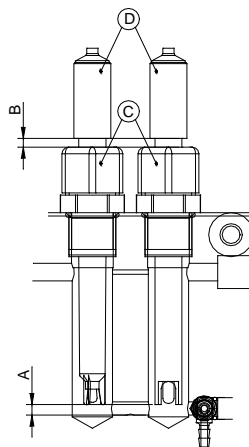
Dettaglio montaggio elettrodi coppia di elettrodi
